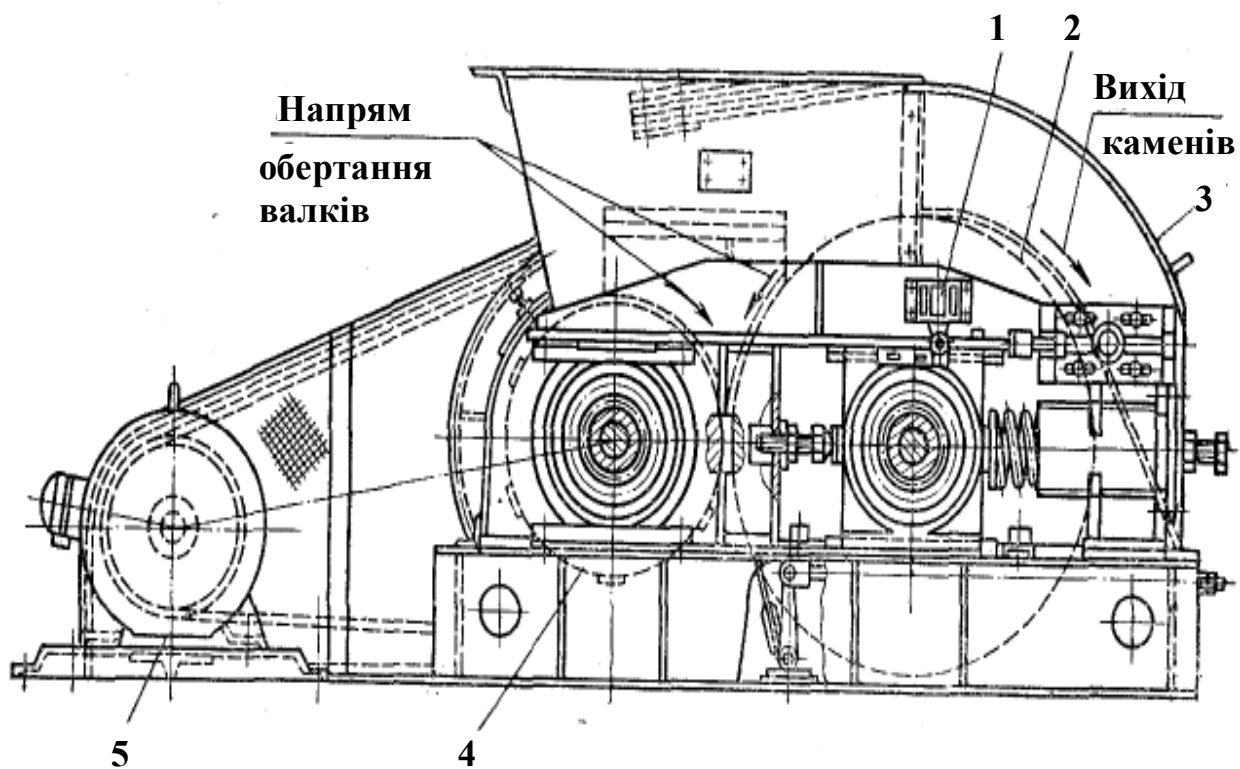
Дезінтеґраторні каменеподібні вальці: 1 – кінцеві вимикачі; 2 – гладкий вал; 3 – кожух; 4 – ребристий валок; 5 – привід ребристого валка
